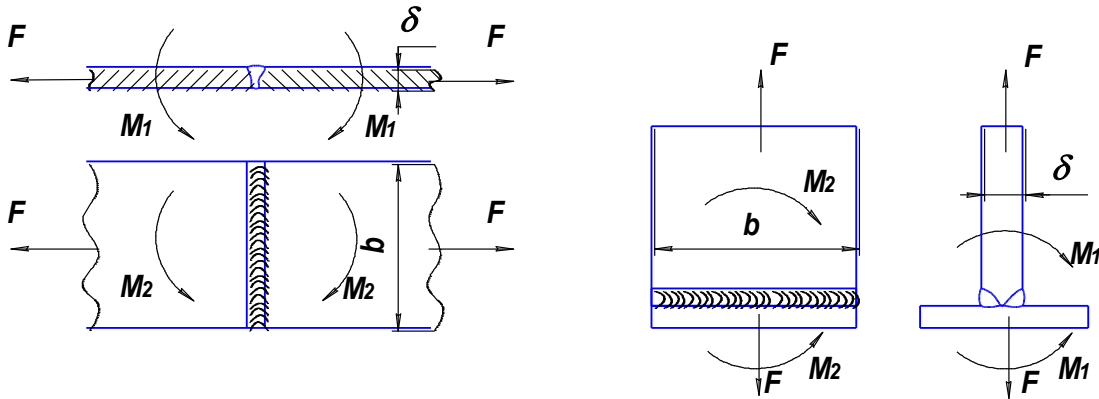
Сварные соединения со стыковыми швами:
